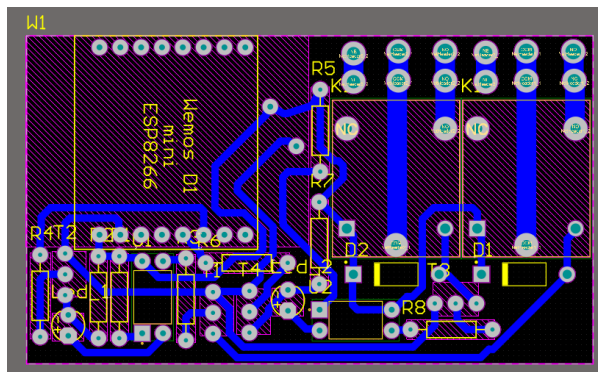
PCB tomacorriente vista pistas de conexión.
